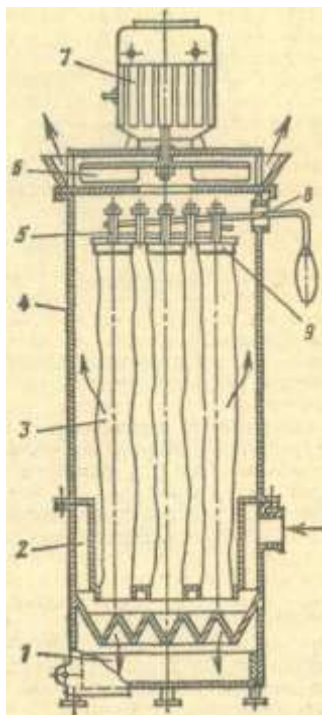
Вентиляционный пылеулавливающий агрегат ЗИЛ-900:
